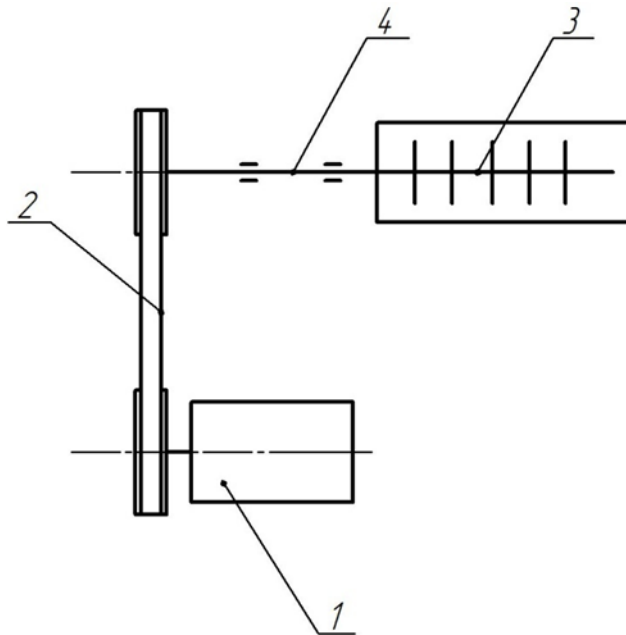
Кінематична система : 1 – двигун; 2 – пасова передача; 3 – ротор; 4 – підшипниковий вузол
